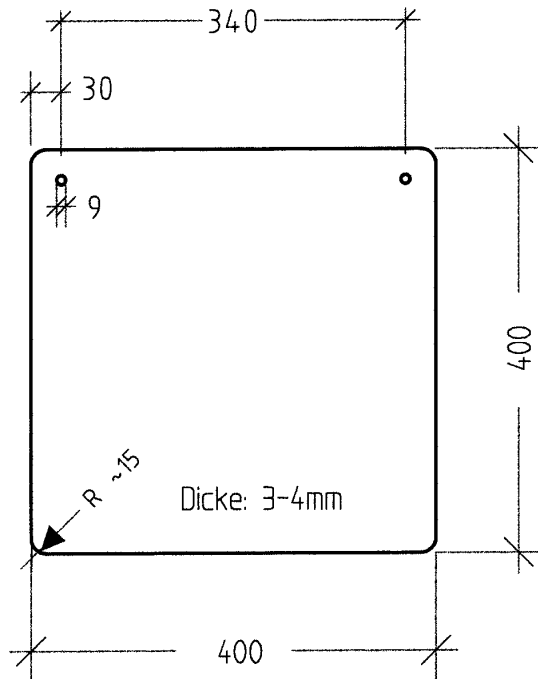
Prüftafel für Langzeitauslagerung mit Bohrungen zur Befestigung
